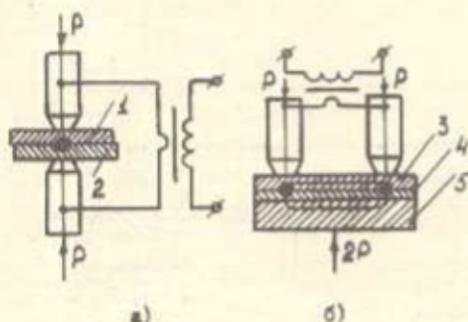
Схема контактной точечной сварки: а) двусторонней ; б) односторонней
